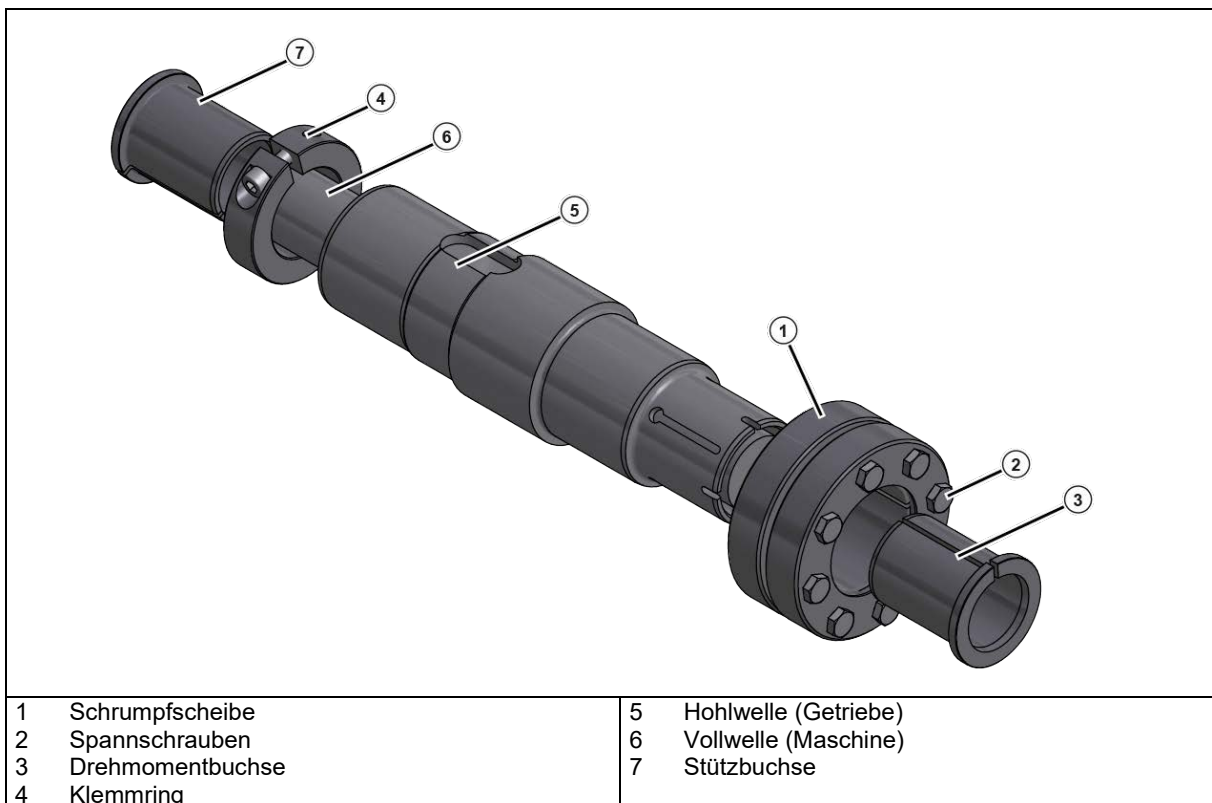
GRIPMAXX™, Explosionsdarstellung
